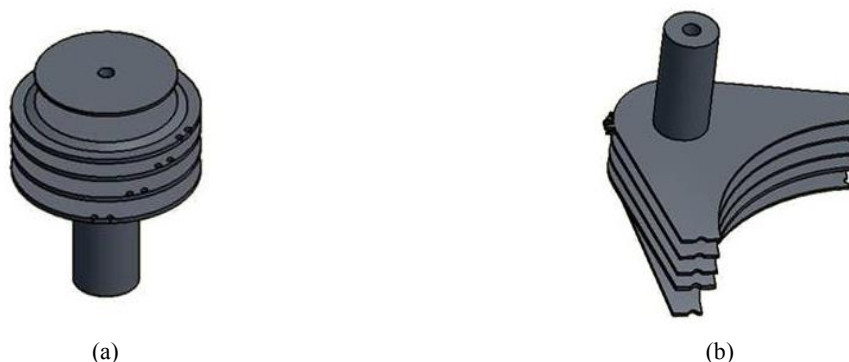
(a) pièce ferromagnétique des bobines centrales, (b) pièce ferromagnétique de l'un des modules externes
